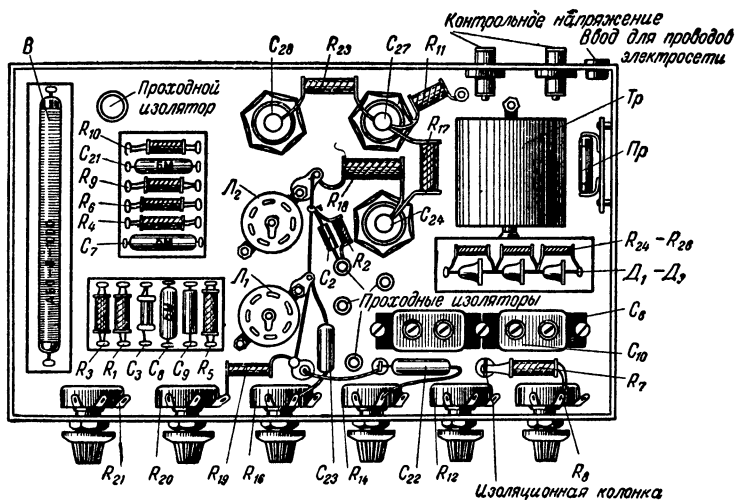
Расположение деталей на шасси прибора (вид снизу).
